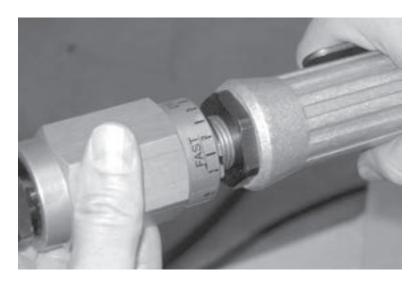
Tournez la bague de commande de la vitesse pour régler la vitesse de rotation de la machine.
